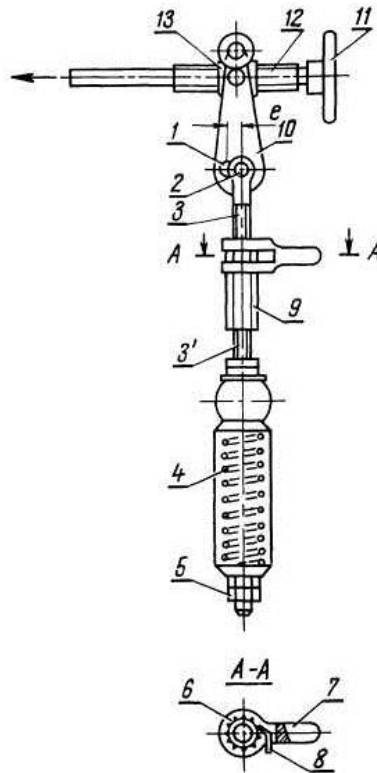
Механізм для регулювання величини зазору між валками вальцьового верстата ЗМ:
